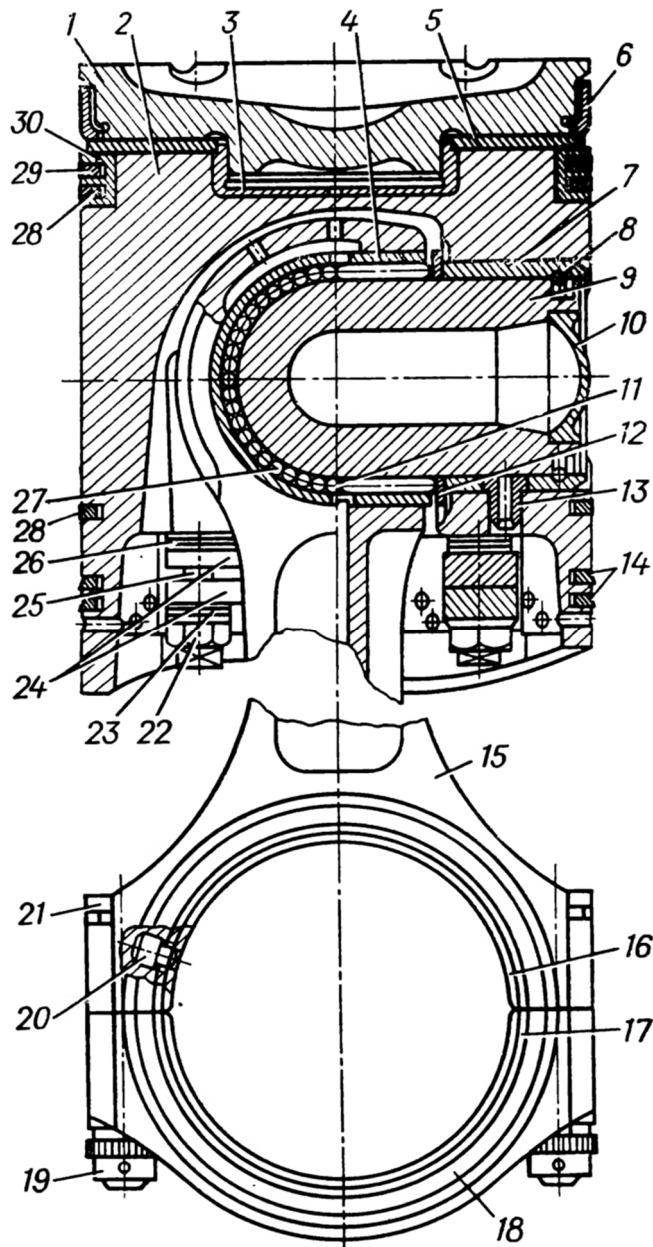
Поршень з шатуном: 1 – накладка; 2 – корпус поршня; 3 – вставка; 4 – втулка верхньої головки шатуна; 5 – проставка; 6 – жарове кільце; 7 – втулка; 8 – стопорне кільце; 9 – палець; 10 – заглушка; 11, 12 – кільця; 13, 20 – штифти; 14 – маслозємні кільця; 15 – шатун; 16 – верхній вкладиш шатуна; 17 – нижній вкладиш шатуна; 18 – кришка; 19, 22 – гайки; 21, 25 – болти; 23, 26 – шайби; 24 – пружина; 27 – ролик; 28 – кільця ущільнювачів; 29 – верхнє кільце ущільнювача; 30 – кільцетримач
